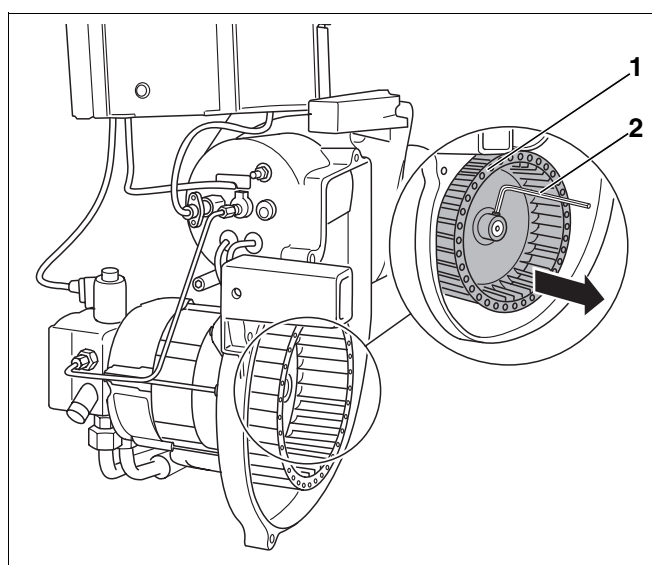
Проверка крыльчатки вентилятора и ее чистка
